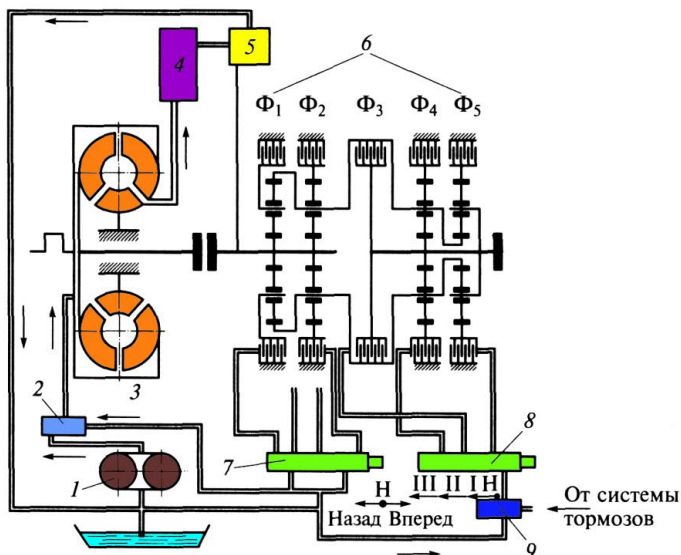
Гидравлическая схема управления гидромеханической планетарной коробкой передач колесного трактора:
